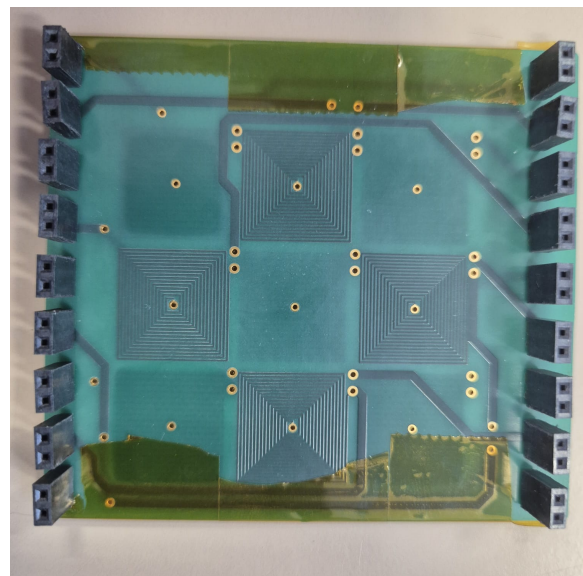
Verso de la carte des bobines complète et assemblée
